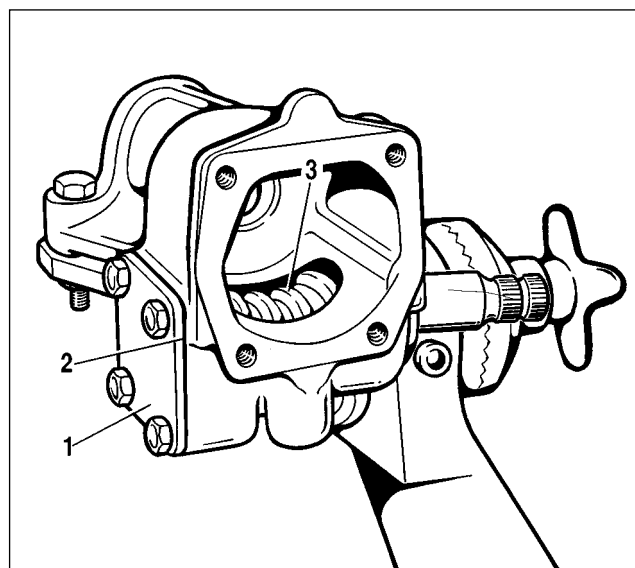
Einsatz der Schnecke des Lenkgetriebes:
